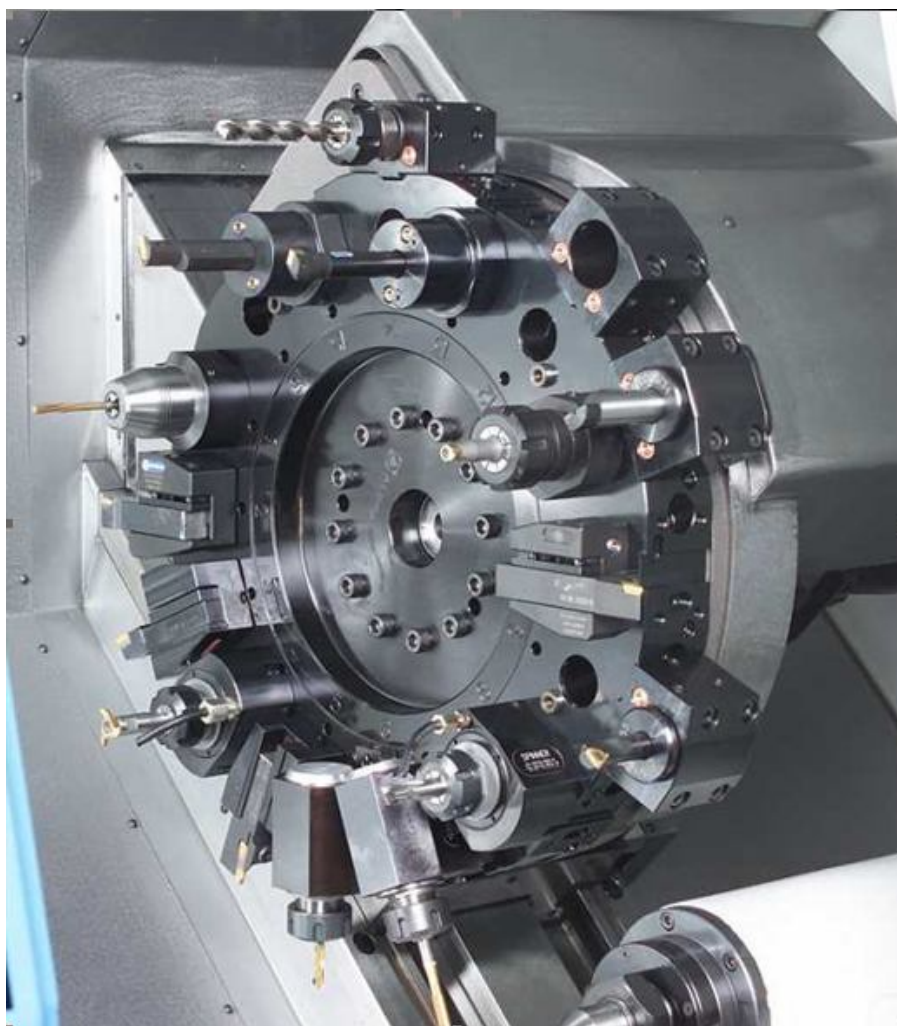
Револьверна головка багатоцільового токарного верстата зі встановленим у ній різальним і допоміжним інструментом
